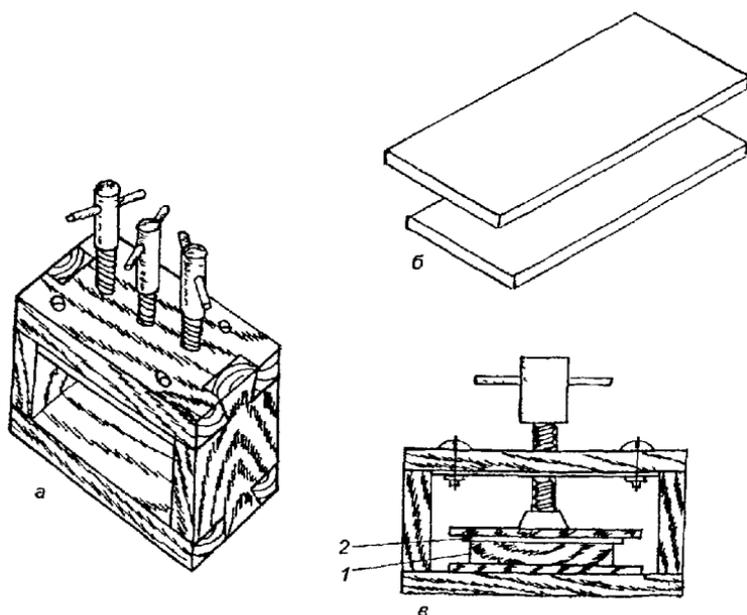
Пресс для наклеивания шпона с запрессовкой
